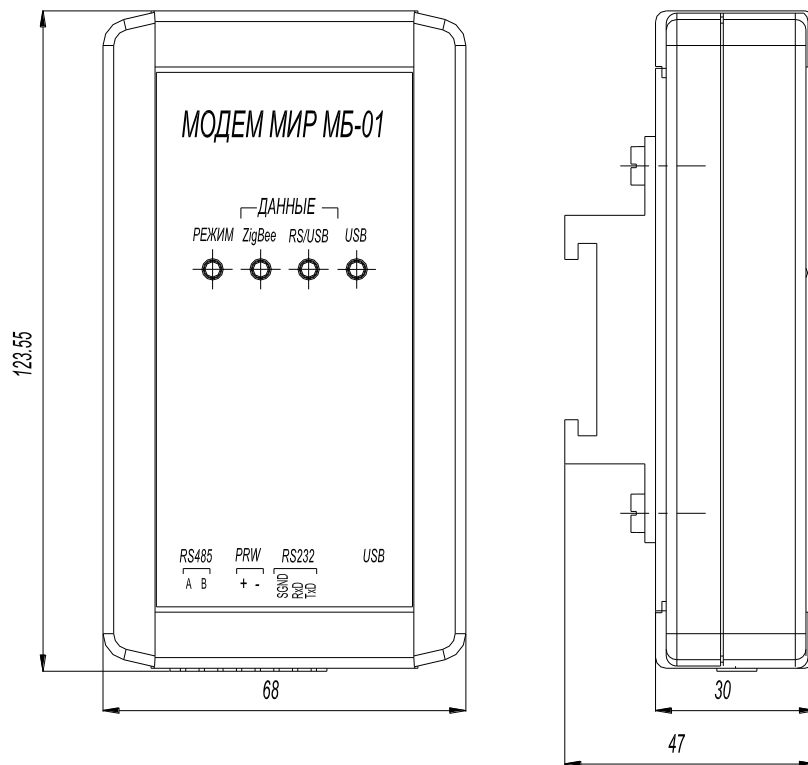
Внешний вид и габаритные размеры модема МБ-01.Д
